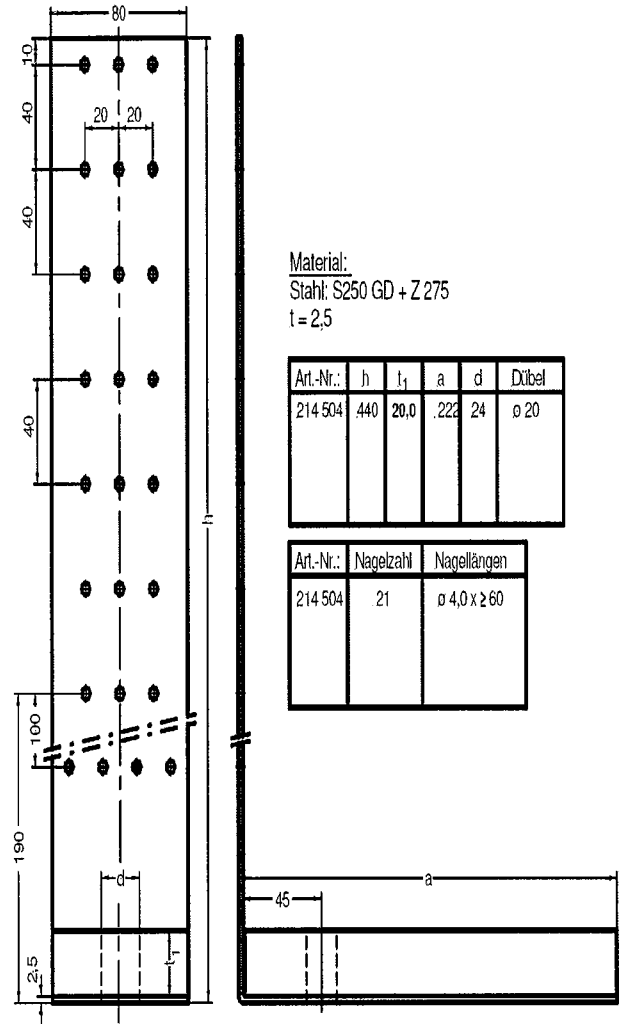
Maße des Zugankers Typ 1; Breite 80 mm
